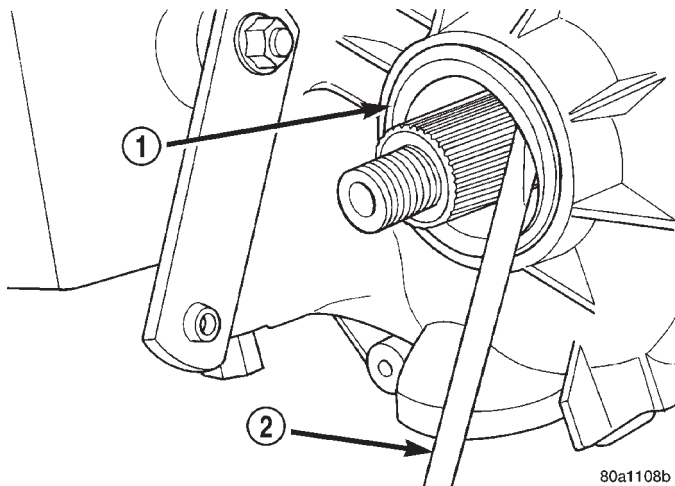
Desmontaje de la junta del eje transmisor delantero
